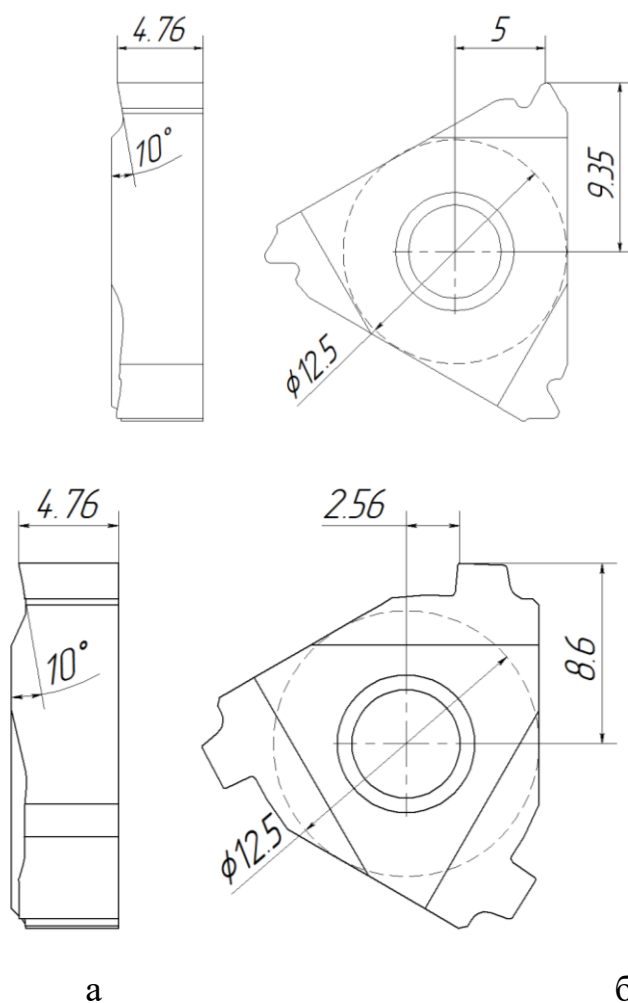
Профили режущих пластин для обработки резьб НКТ 73 (а) и упорной резьбы Buttress (б)
